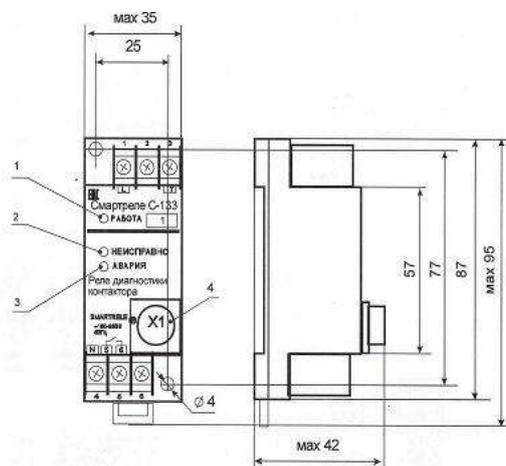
внешний вид, габаритные и установочные размеры СМАРТРЕЛЕ С-133
